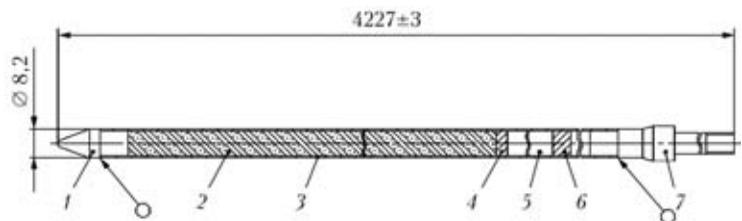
Схема ПЭЛа: 1 — конус (заглушка); 2 — наполнитель (порошок карбида бора); 3 — оболочка; 4, 6 — пробки; 5 — утяжелитель; 7 — наконечник
